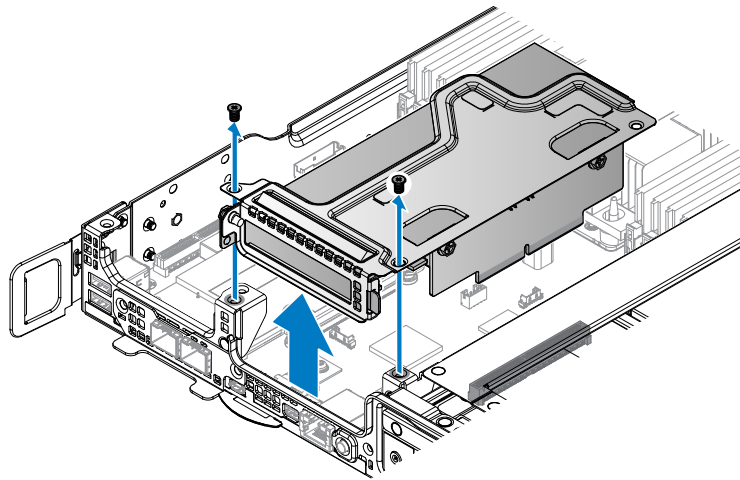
Entfernen der PCIe-Kartenbaugruppe
